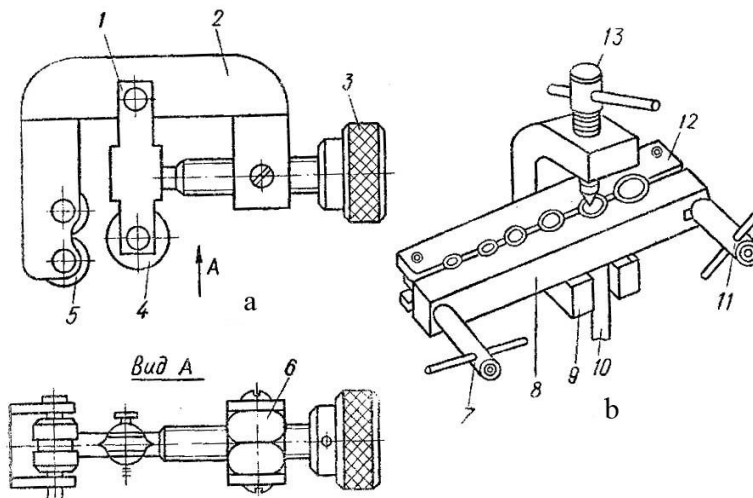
Труборіз (а) і пристрій ПТ-265.10 для розвальцьовування трубок (b): 1 – поводок; 2 – корпус; 3 – гвинт; 4 – ролик; 5 – ніж; 6 – гайка; 7, 11, 13 – гвинти; 8, 12 – планки; 9 – скоба; 10 – розвальцьована трубка
